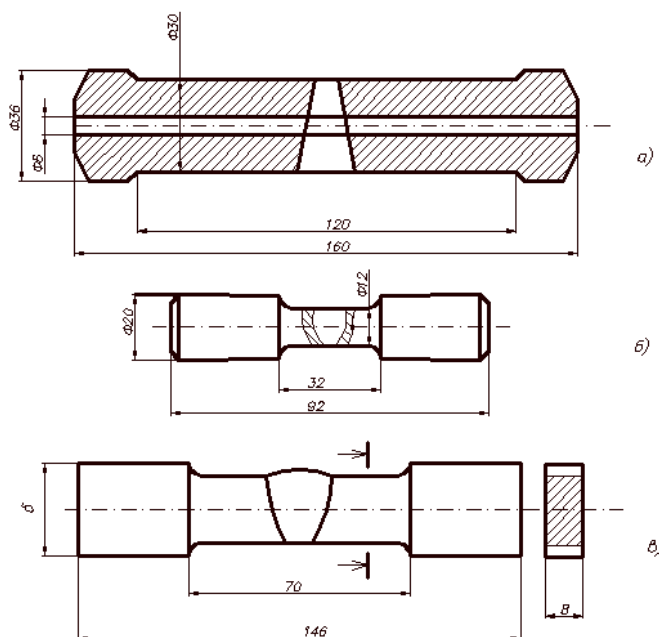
Сварные образцы для испытаний на длительную прочность и пластичность с целью оценки склонности к ТТО [4]: а – трубчатые образцы; б – цилиндрические образцы; в – плоские образцы
